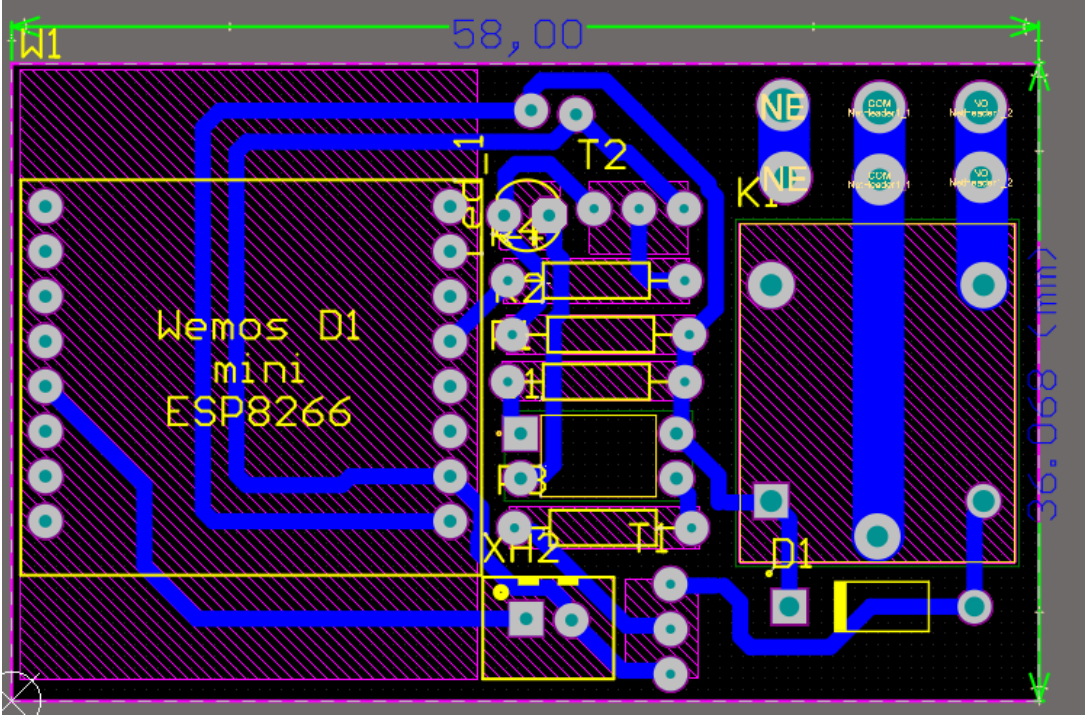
Dimensiones Placa PCB módulo Interruptor.
